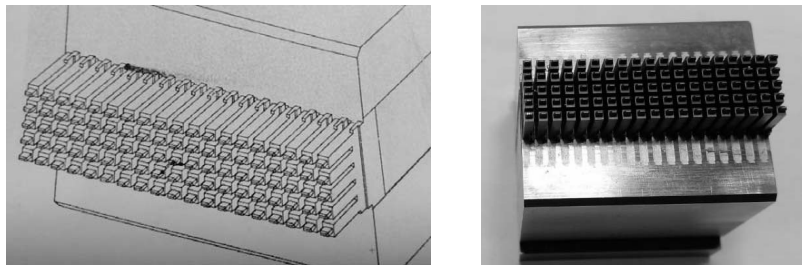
Конструкторская схема сварки и внешний вид изделия после сборки
